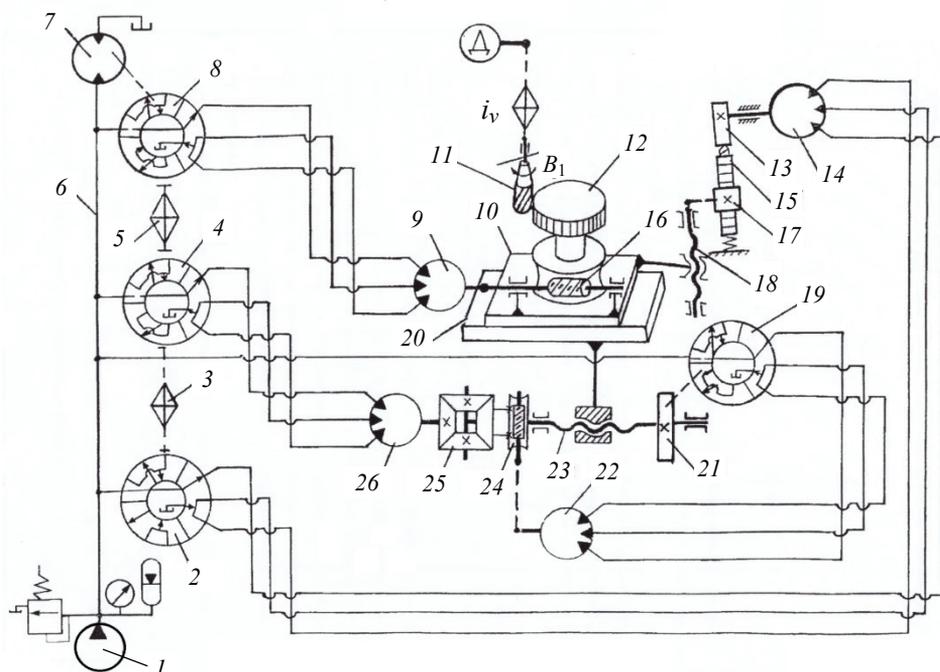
Структурная схема копировально-фрезерного станка с гидравлическими формообразующими связями для обработки деталей со сложными поверхностями, типа дисковых кулачков с модифицированной системой управления
